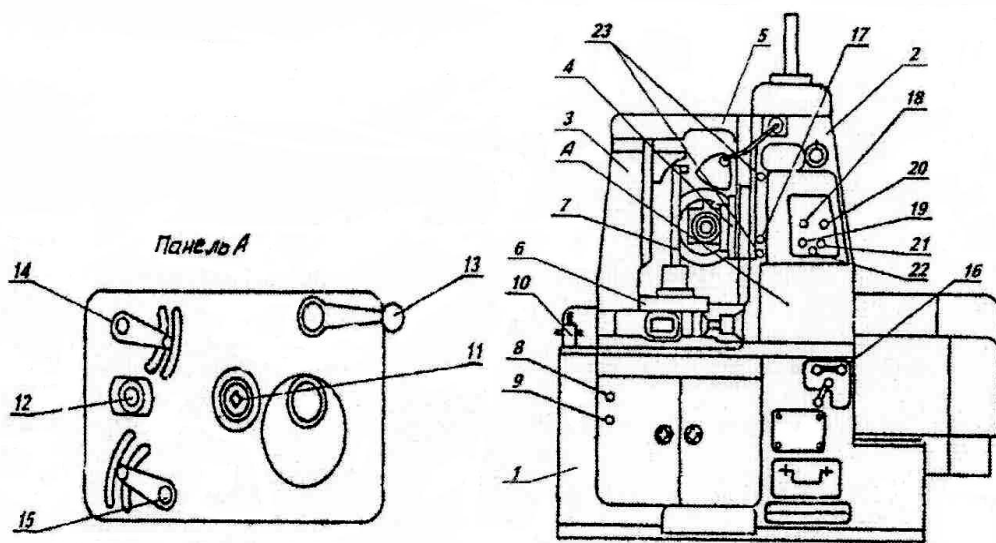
Общий вид зубофрезерного станка мод. 5310
